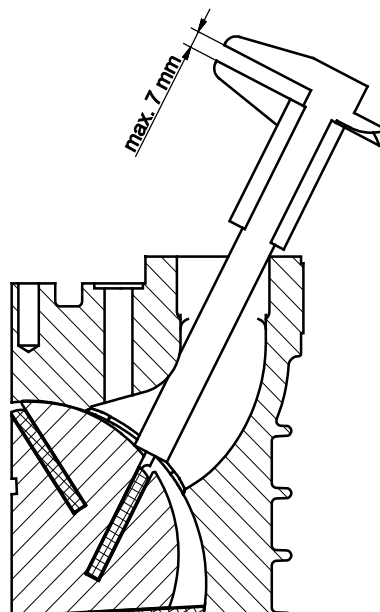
Mesure de l'usure de la hauteur des coulisses du rotor
